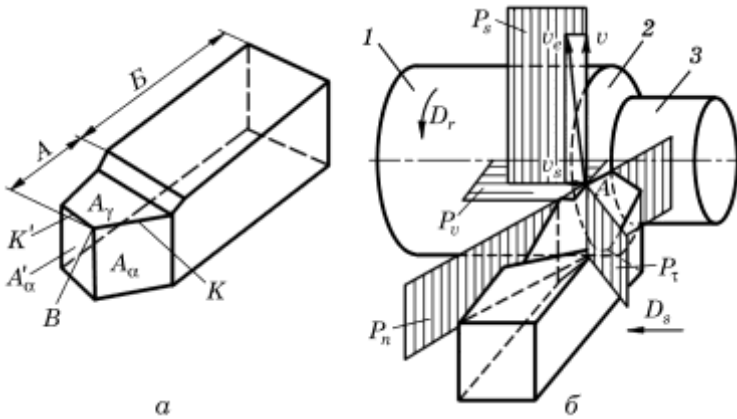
Елементи прохідного токарного різця (а), поверхні заготовки та координатні площини (б)
